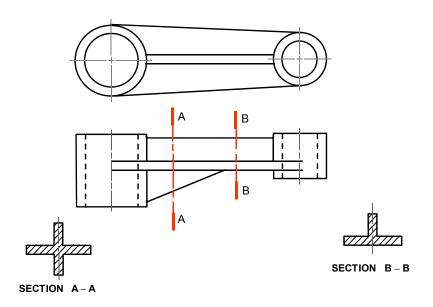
เปรียบเทียบภาพตัดแบบ revolved และ removed section
